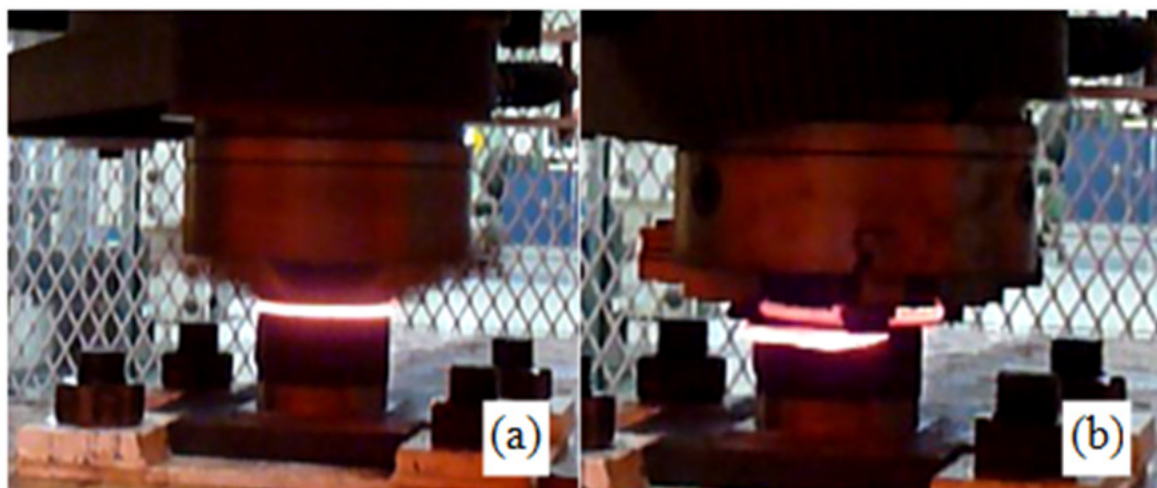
Início da soldagem (a) e desalinhamento da máquina (b).
